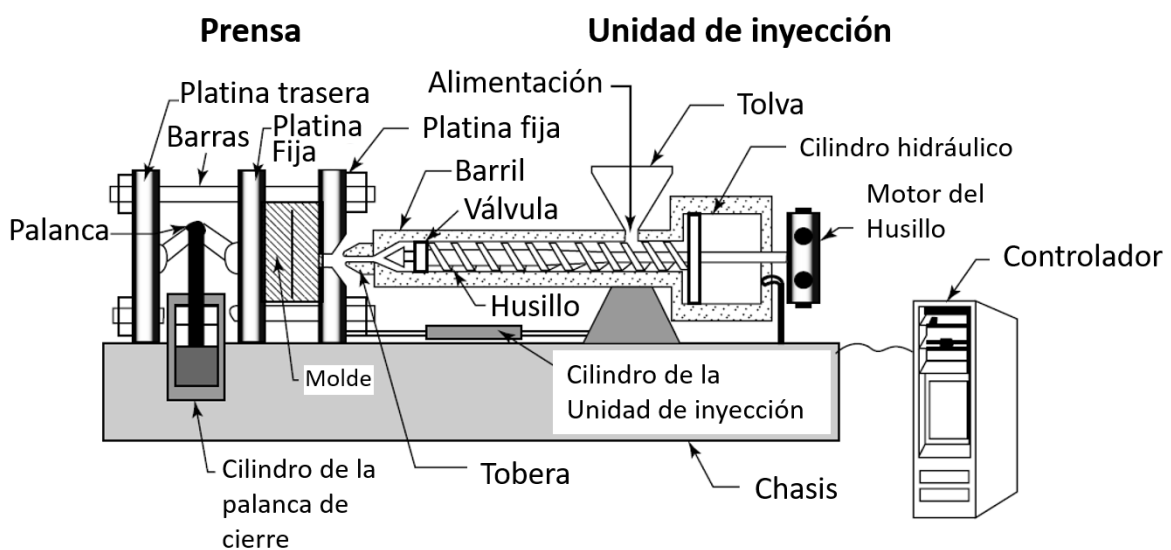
Esquema de una máquina de moldeo por inyección (Mark, 2004:5)
